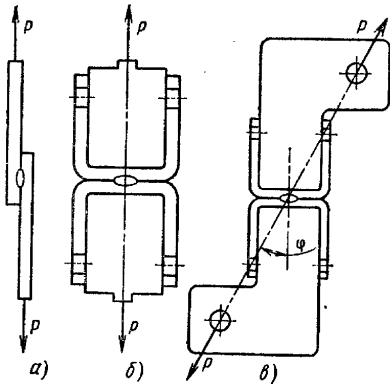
Схема испытаний точечных сварных соединений:
